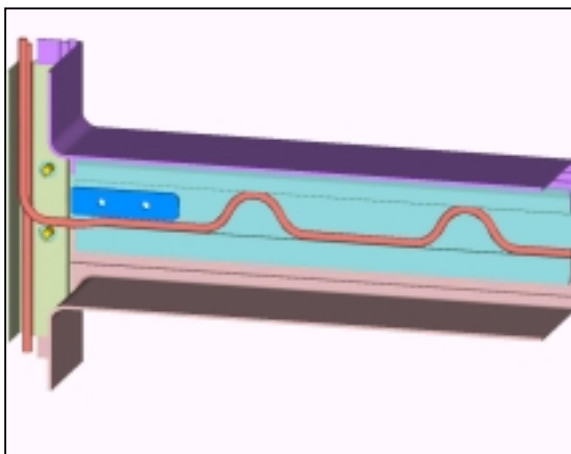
Figura A: Vista frontal da montagem do conjunto Travessa Intermediária.
